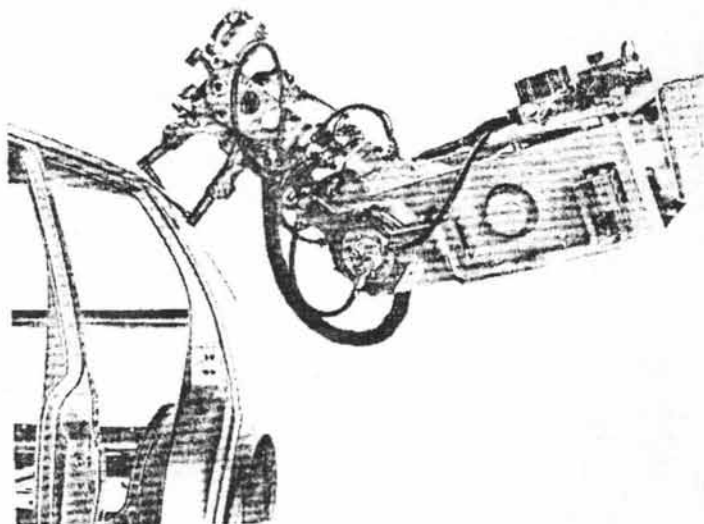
, Brazo robot que realiza soldadura de puntos
